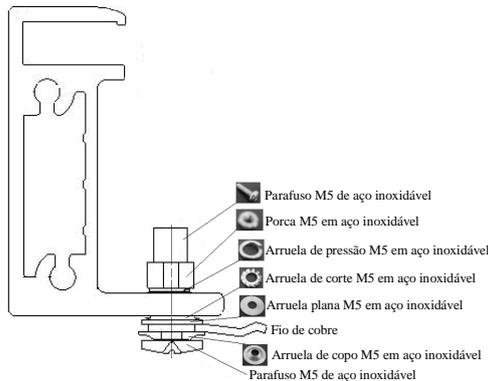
Aterramento da moldura de alumínio com fio de cobre
